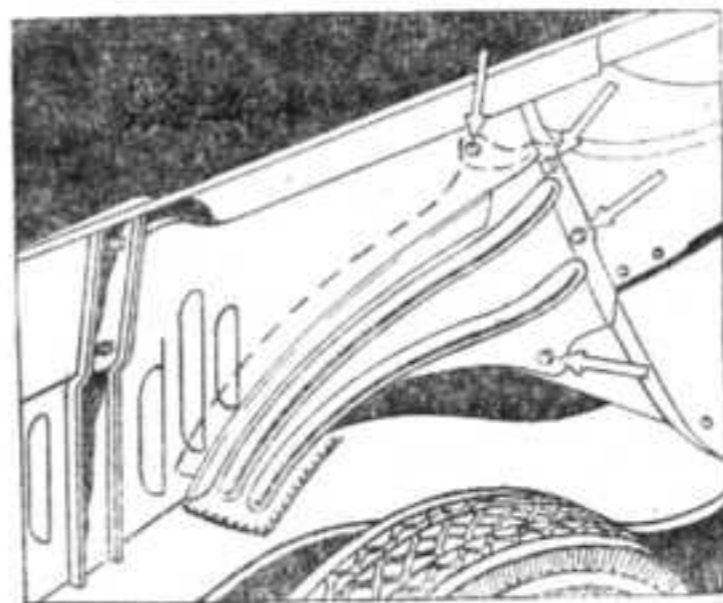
Корпус кузова с привернутой к нему рамой.
